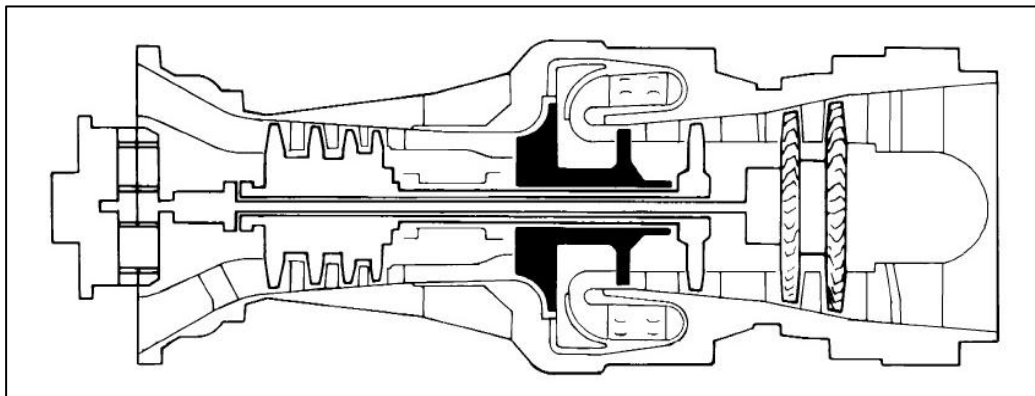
Turboeje con cámara de combustión de flujo reversible [5]
